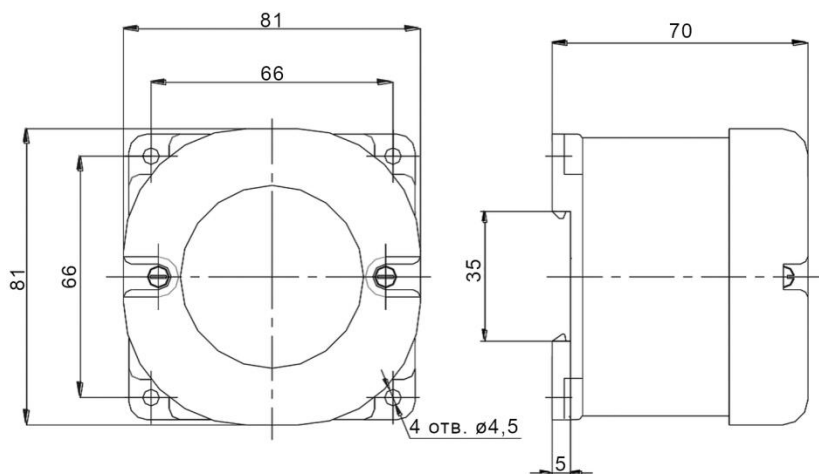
Габаритные и установочные размеры устройства M22.003.00.000
